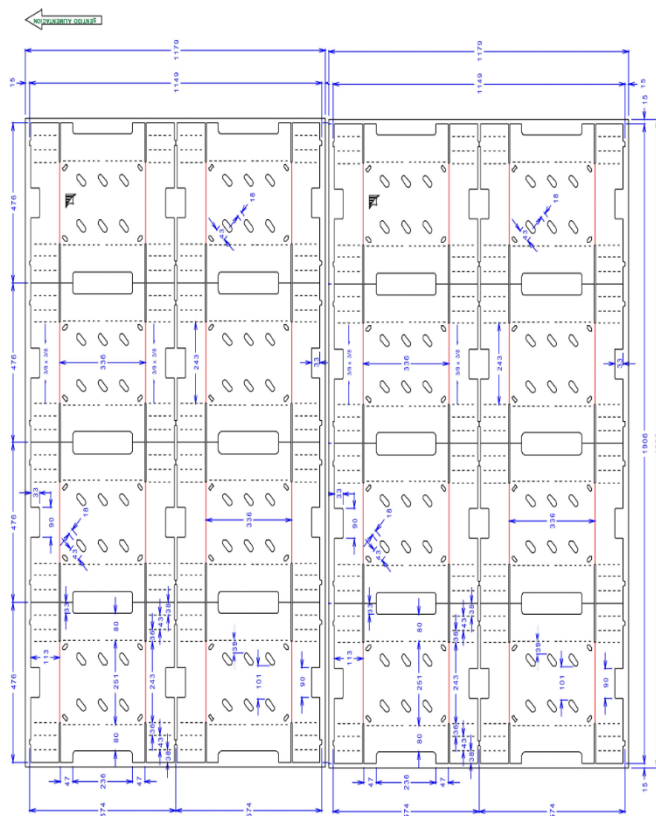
Ancho útil en la planificación de mango de 2.338m
